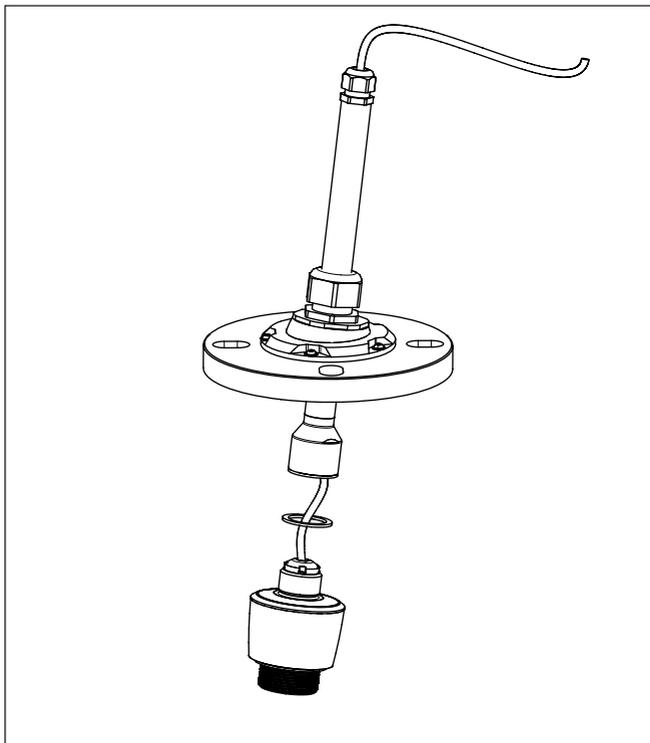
Montaggio del dispositivo di allineamento con flangia universale
